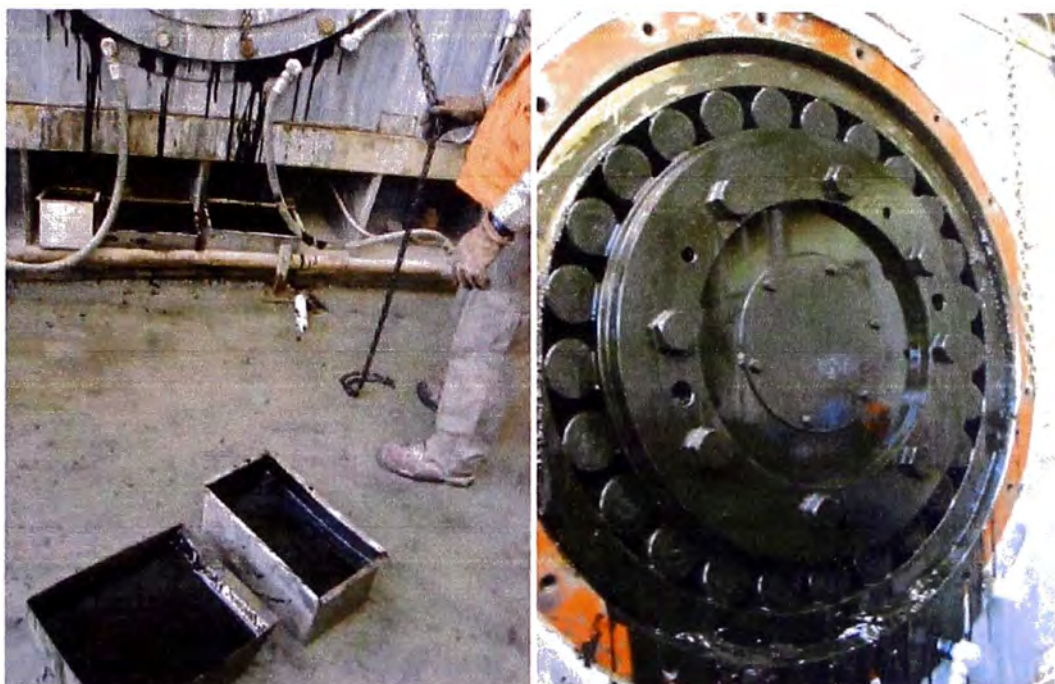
Inspección del estado de rodamiento exterior (B) de HPGR N°33.
